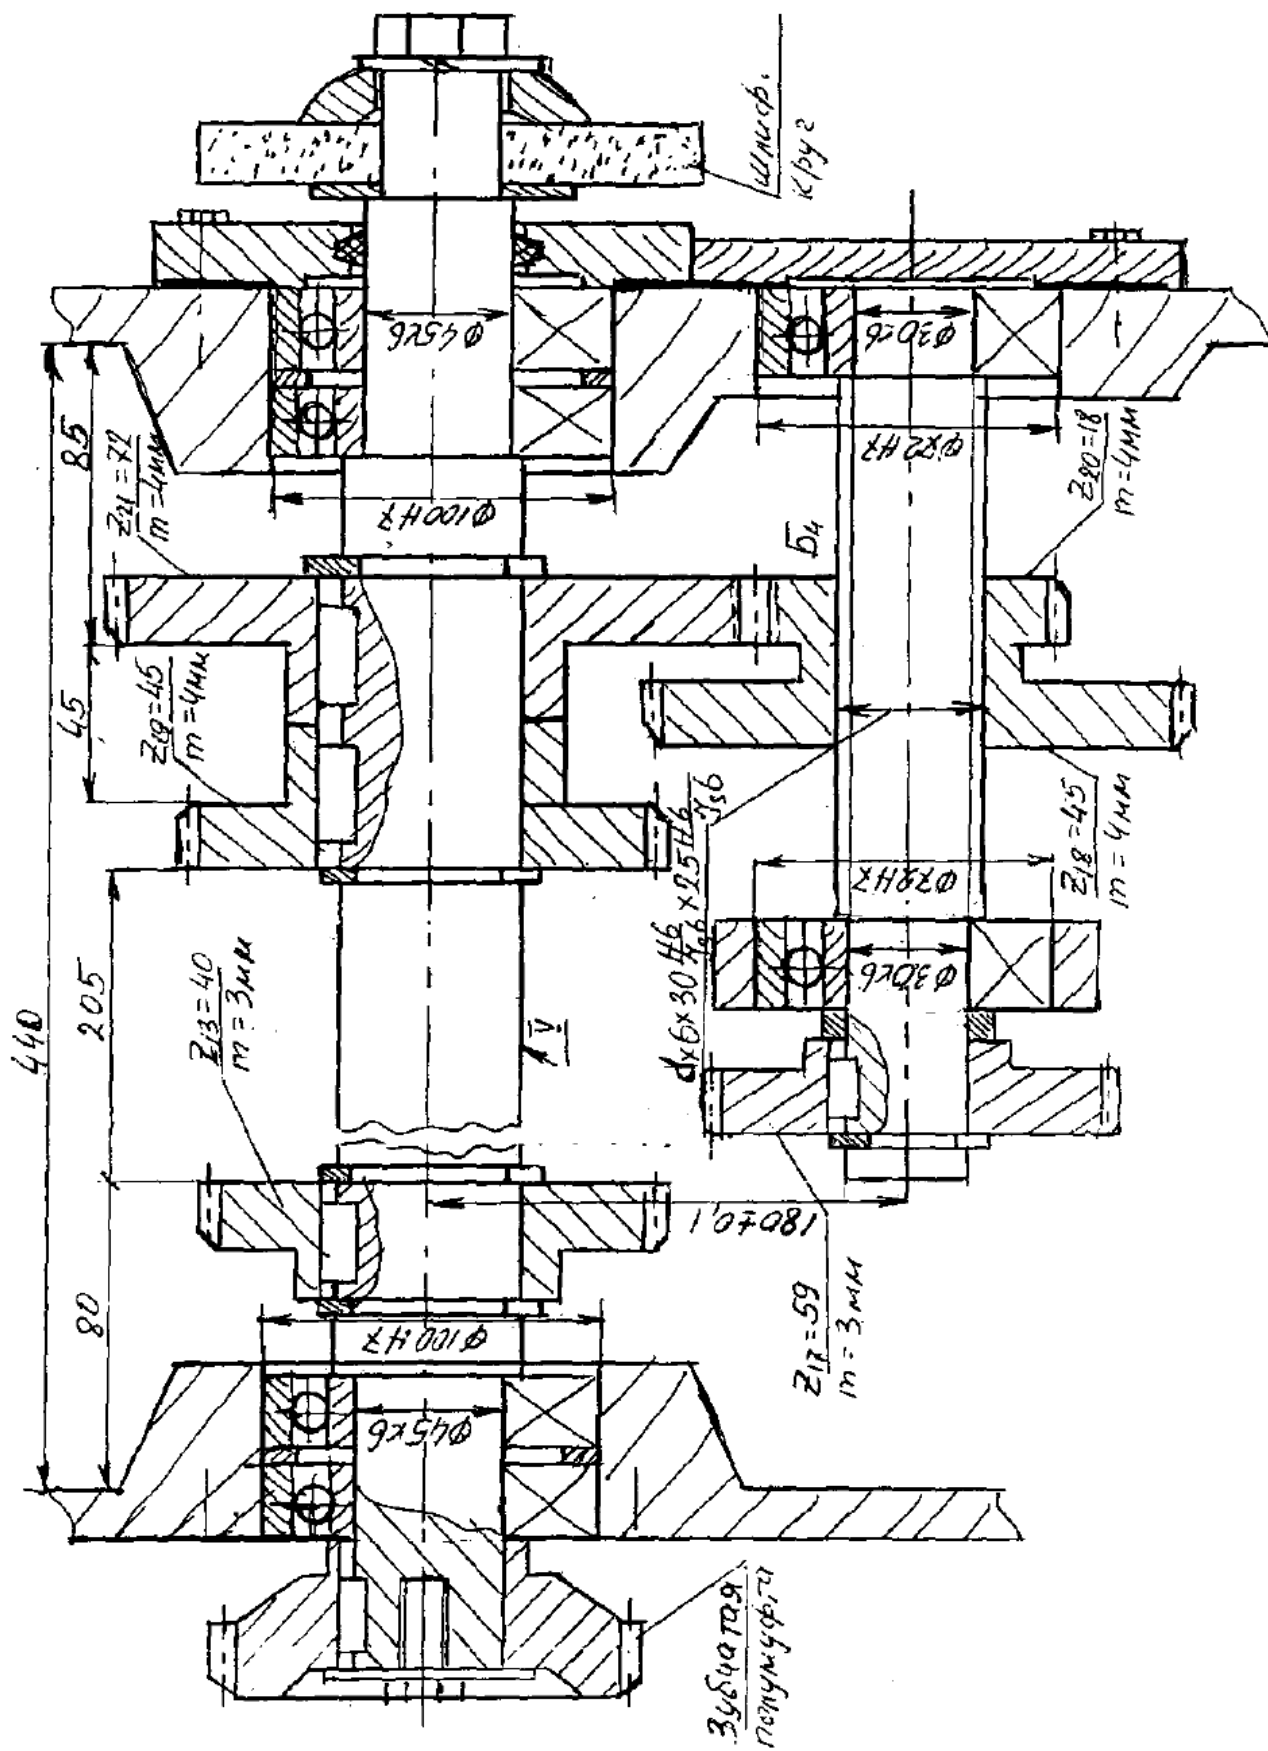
Сборочный чертеж наиболее нагруженной группы передач
